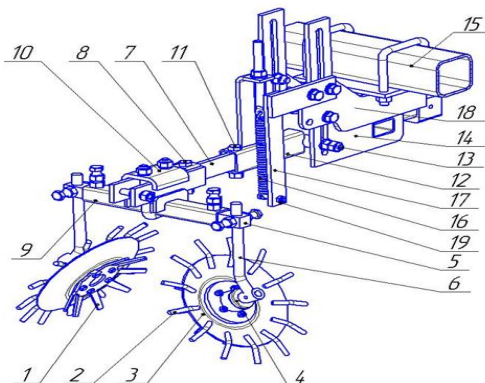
Секция фрезерных дисков для обработки боковых поверхностей гряд
